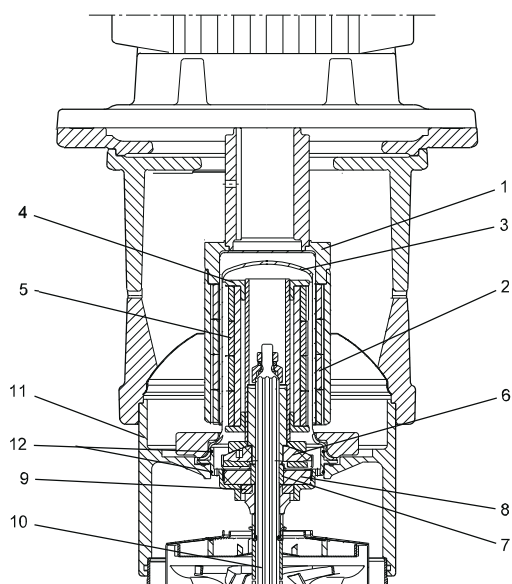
Schnittzeichnung der Magnetkupplung MAGdrive
